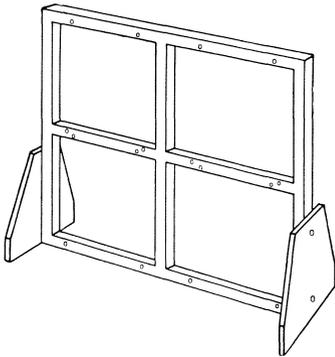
Gestell für die Panelplatten des Radiobaukastens.
